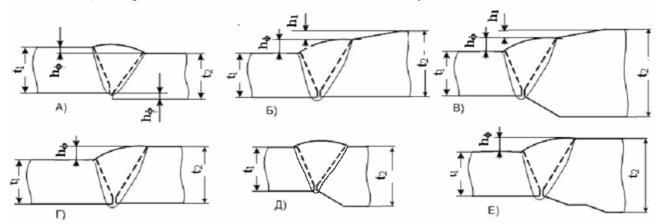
Смещение кромок (a); разнотолщинность в сварных соединениях (б; в; г; д; е;)
